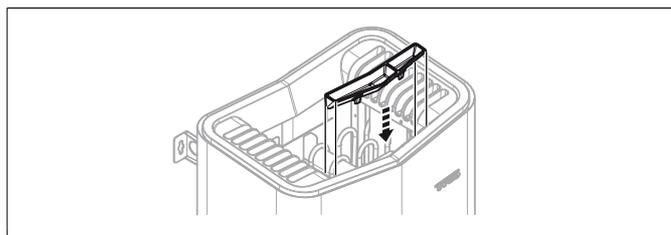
Установка подставка для флакона с ароматизатором/увлажнителя воздуха
